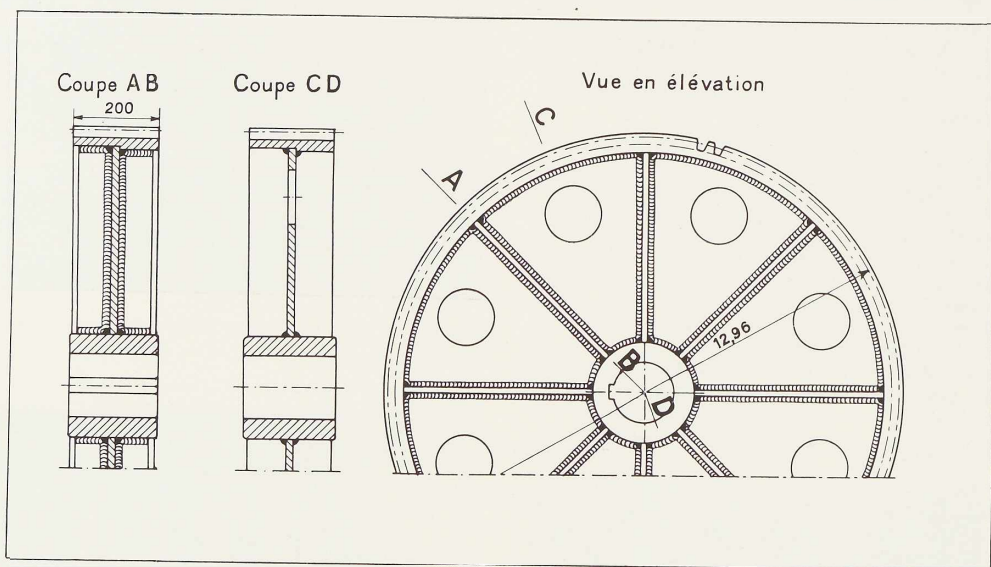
Elévation et sections d'un engrenage de pont roulant construit à l'aide de pièces d'acier soudées.
